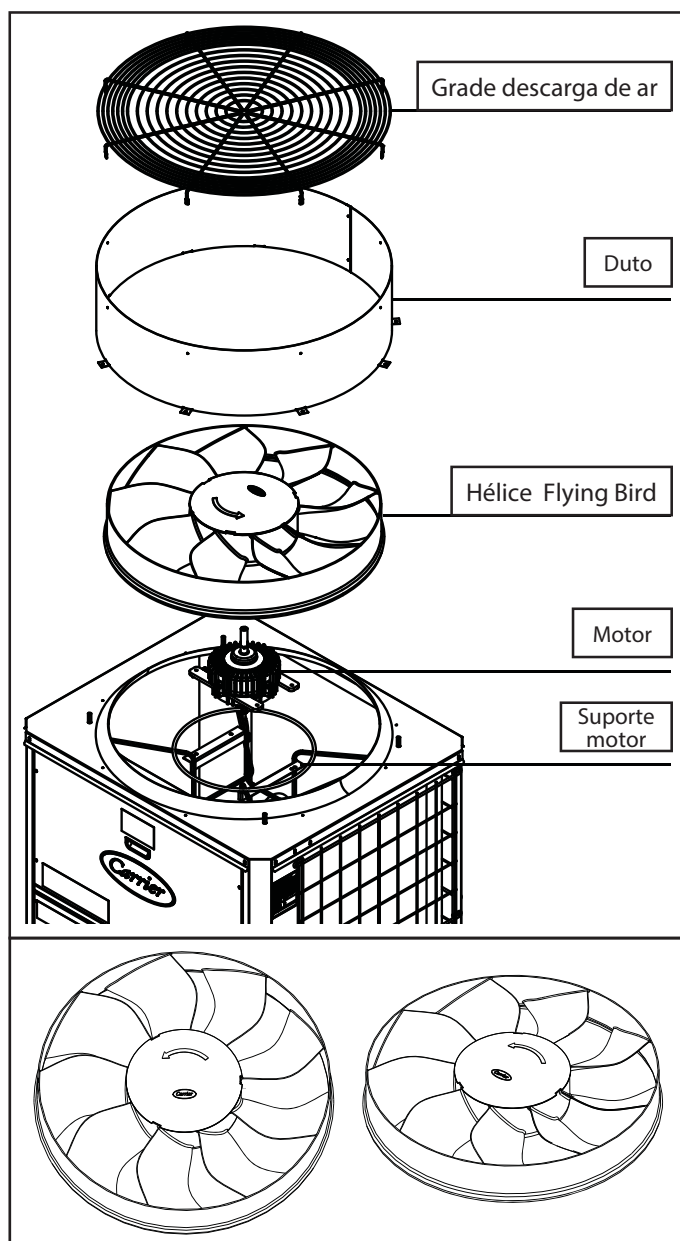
Vista explodida conjunto ventilador condensadora e Hélice Flying Bird
